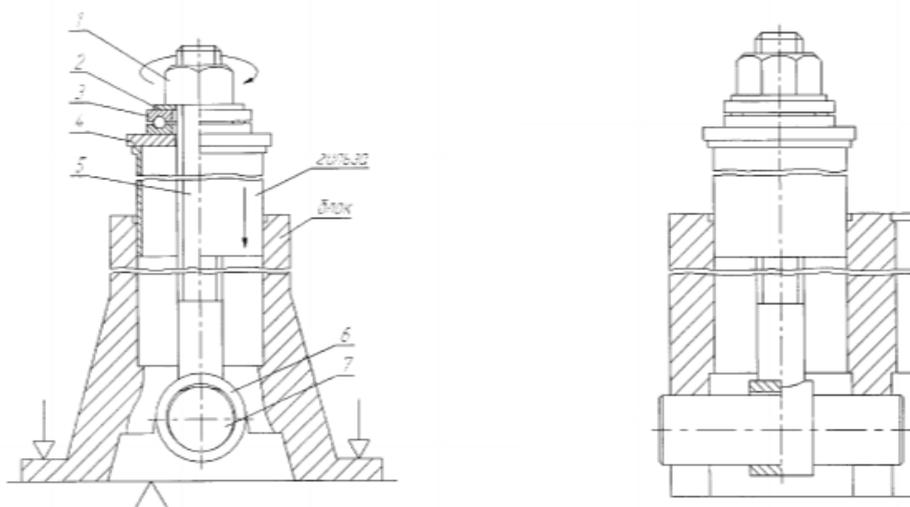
Устройство для запрессовки гильз в цилиндры
